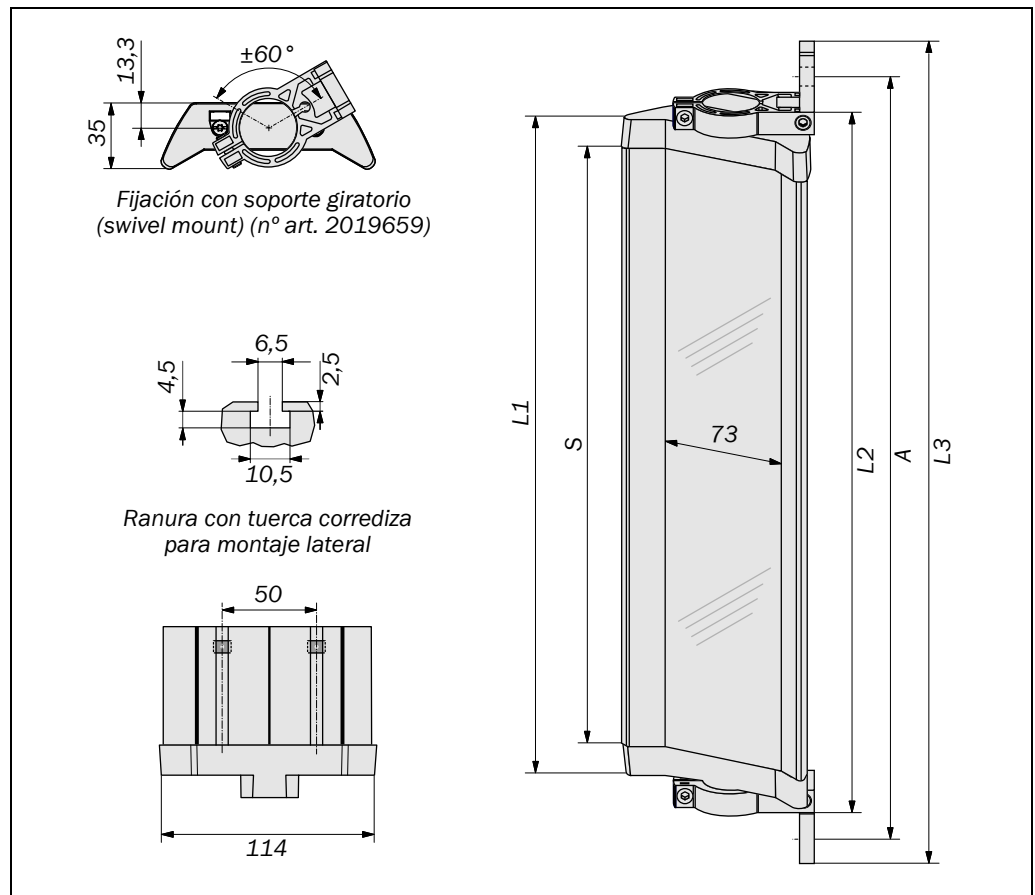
Croquis de dimensiones soporte C-Fix-Flex, orientable (mm)
